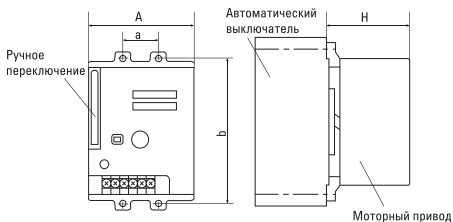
Габаритные размеры моторного привода к ВА-99М 400, 630, 800
